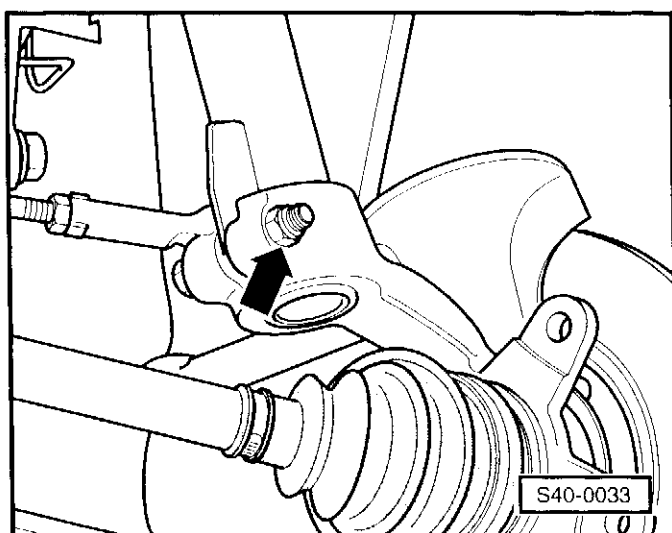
Разборка соединения между крышкой подшипника ступицы колеса и амортизатором
